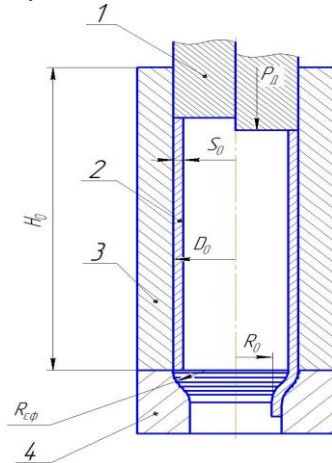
Схема обтиску трубчастої заготовки в профільованій матриці (1-пуансон, 2 - заготовка, 3 - оправка, 4 - матриця )
